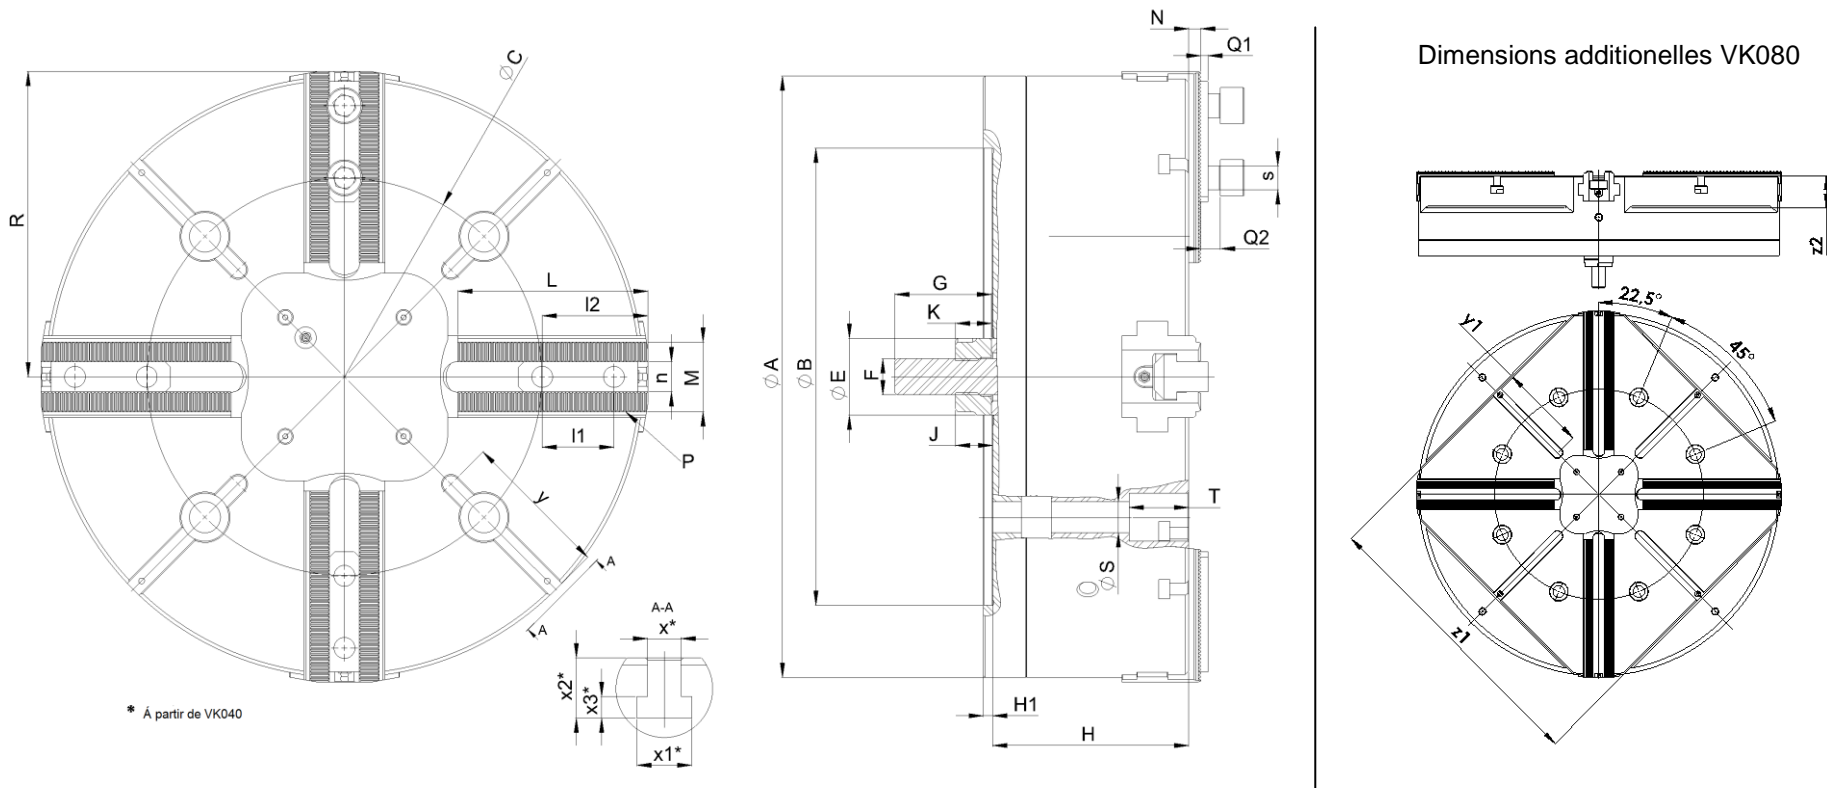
Dimensions de raccordement VK021 - VK080
